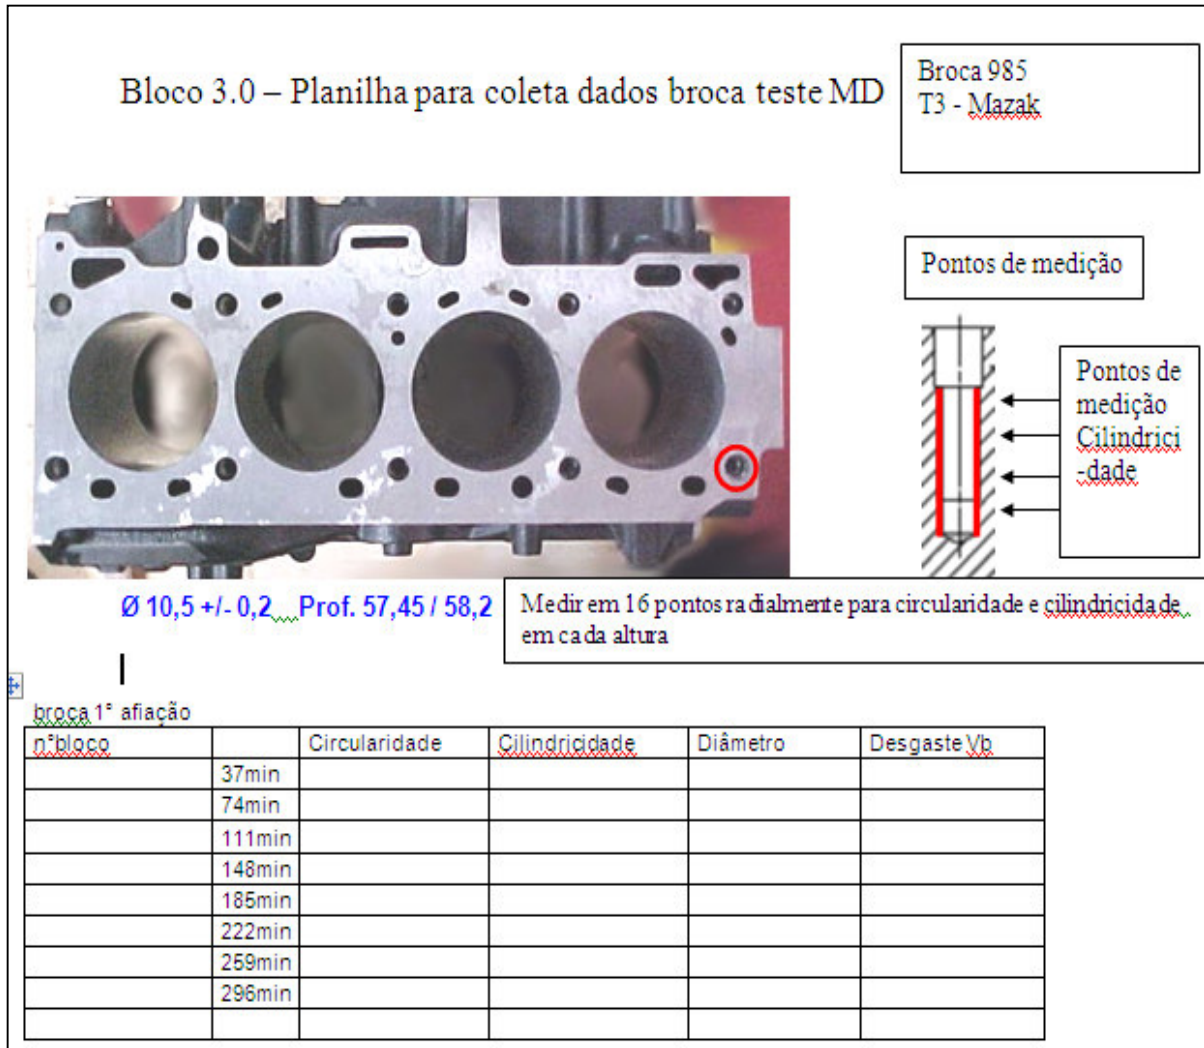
Planilha de registro e orientação das medições do ensaio
